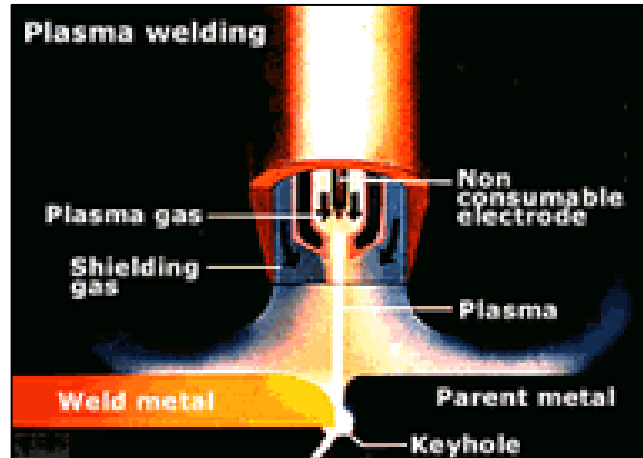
6: Diagrama esquemático del proceso de soldadura PAW
